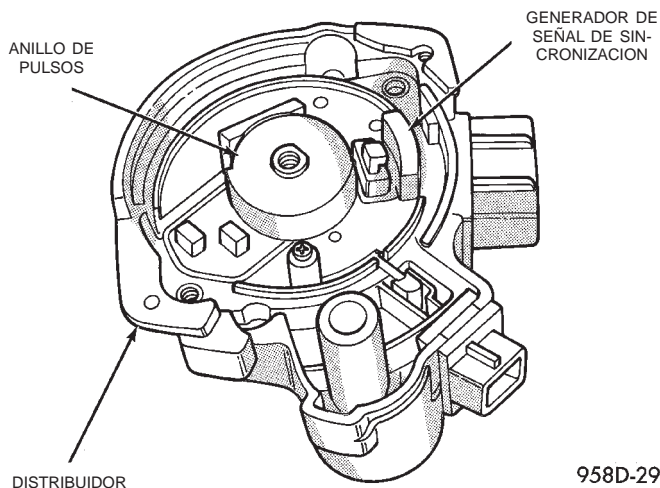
Sensor de posición del árbol de levas—motor de 2.5L
